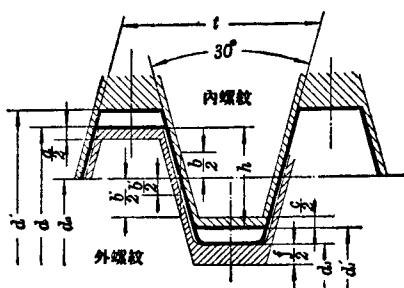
2级、3级精度梯形螺纹公差带位置的配置
